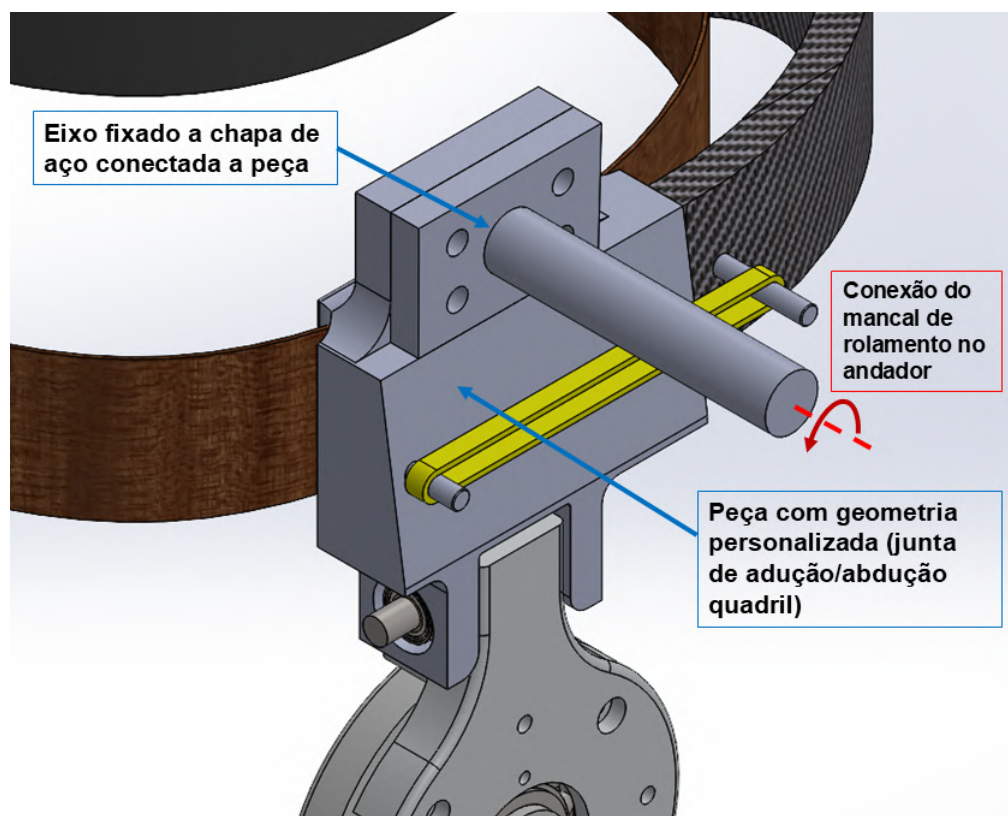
Montagem e mecanismo de conexão Exo-Andador
